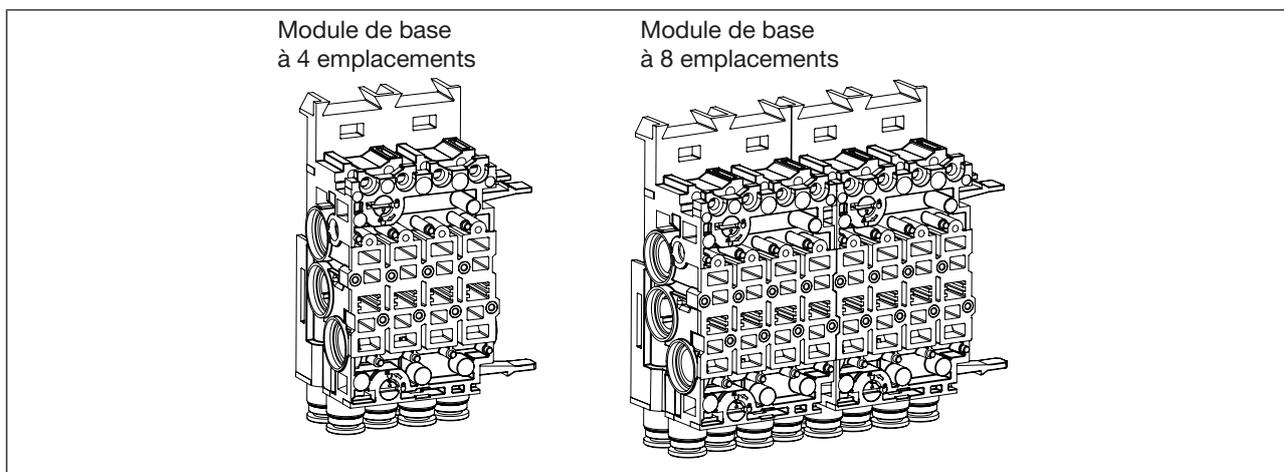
Vue d'ensemble du module de base pneumatique (illustré : REV.2 - différences de détails uniquement par rapport à REV.1)
